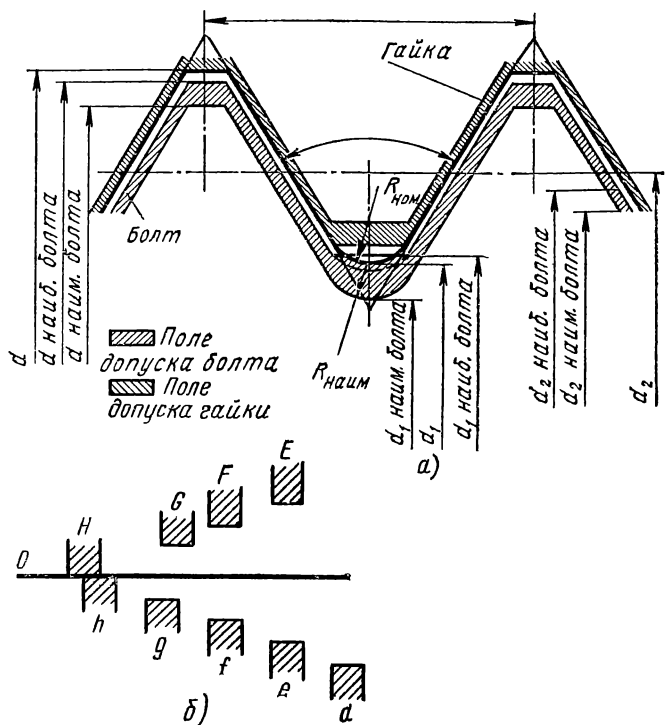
Схема расположения полей допусков болта и гайки:
